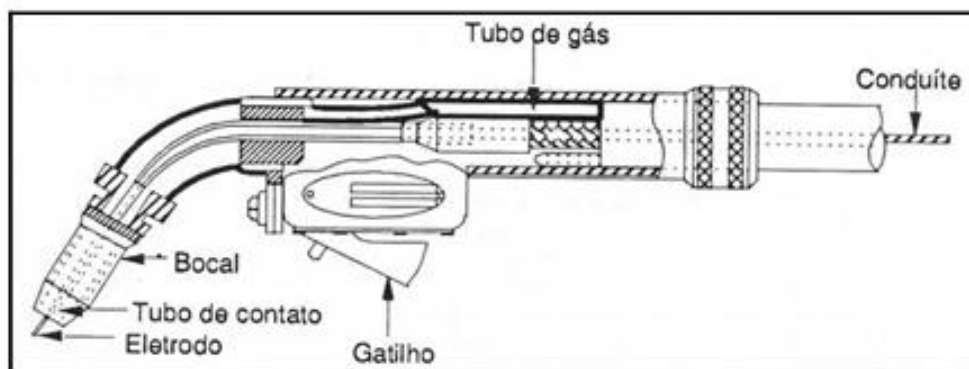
Esquema de uma tocha para soldagem MIG/MAG.
